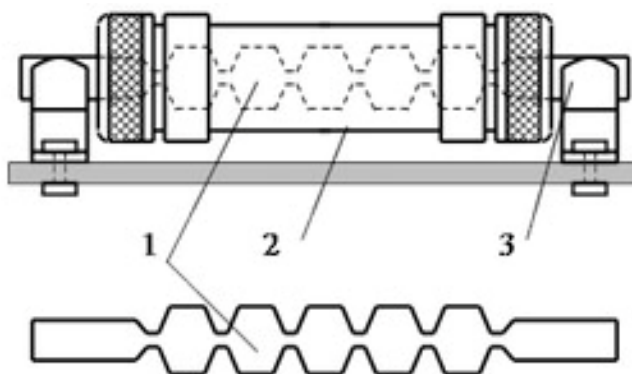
Плавкий запобіжник: 1 - плавка вставка; 2 - корпус; 3 - контакти
